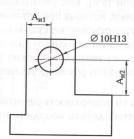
Эскиз обрабатываемой детали к заданию 1.28
